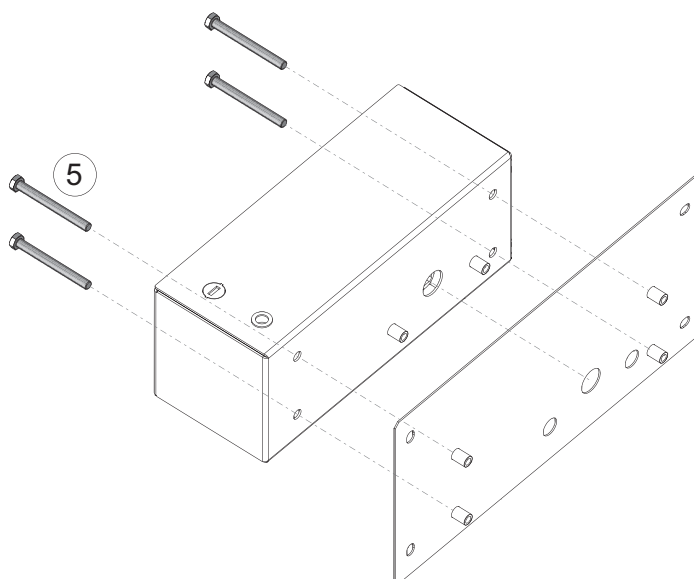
Boîtier de commande et couvercle du silo vissés ensemble
